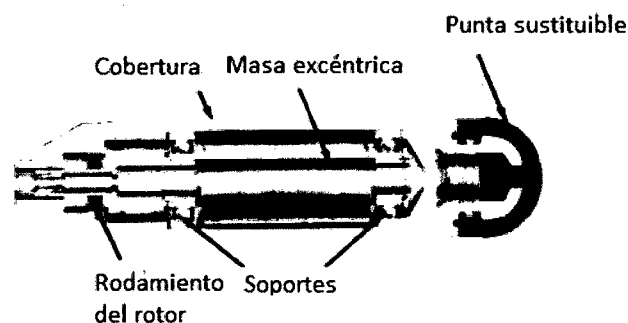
Partes de la cabeza vibradora de masa excéntrica.
